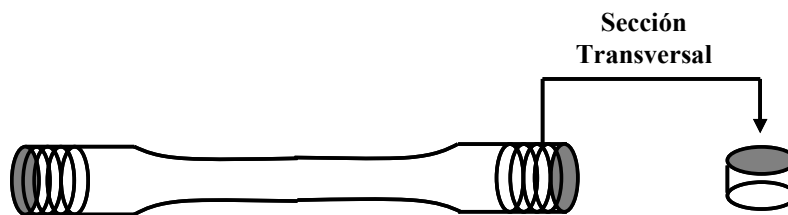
Corte transversal de la zona de la rosca realizado en cada probeta antes de ser ensayada.
